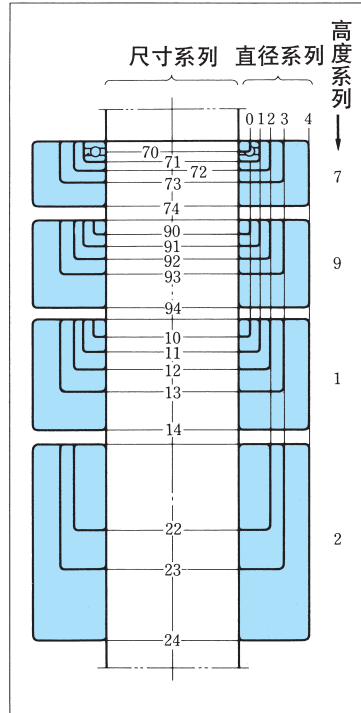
推力轴承的尺寸系列 (省略直径系列 5)
